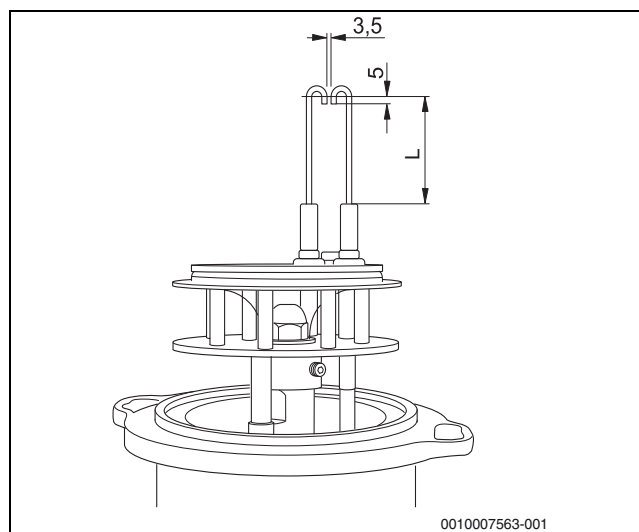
Elettrodo di accensione (dimensioni in mm)
